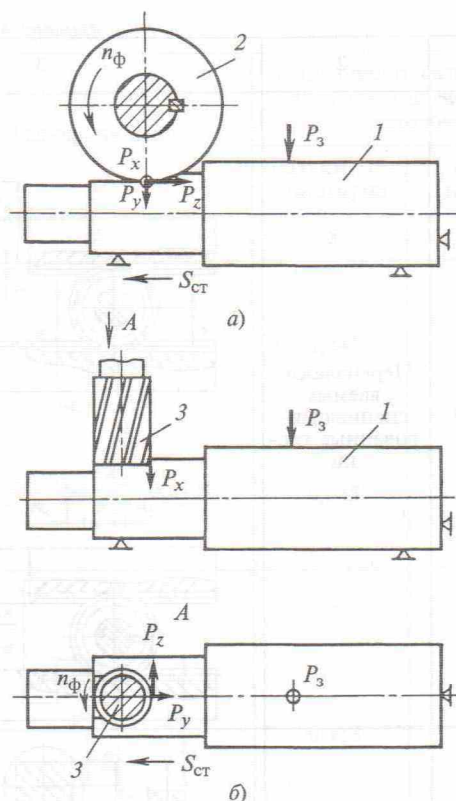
Схемы сил резания при фрезеровании цилиндрической (а) и концевой фрезями (б):
